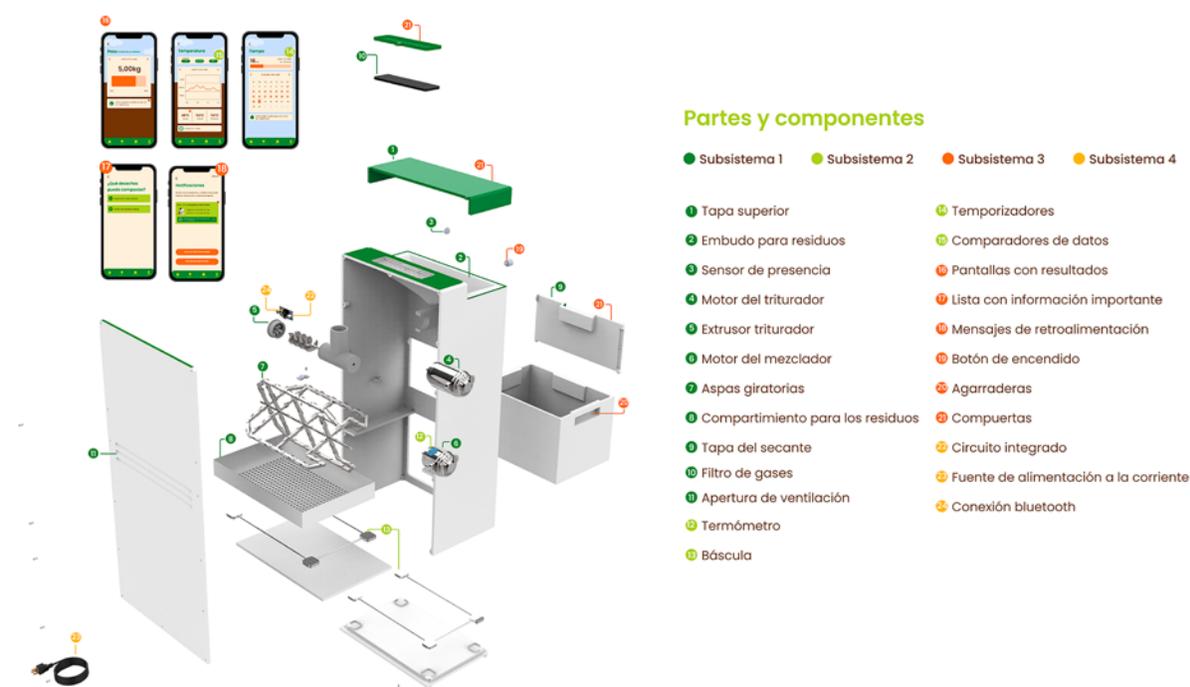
Explosión de partes y componentes que conforman el dispositivo.
